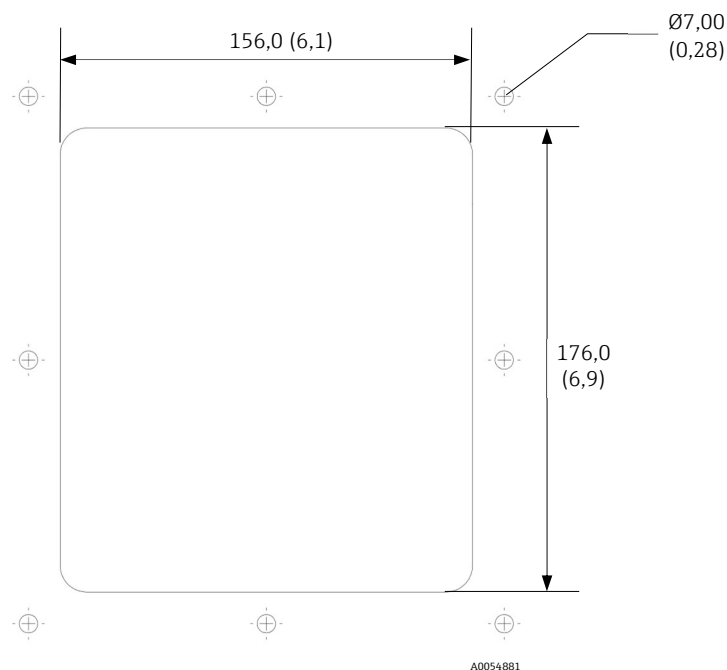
Вырез для монтажа в корпусе. Размеры: мм (дюймы)
